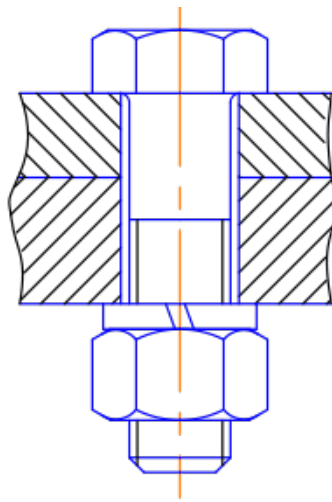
Corte de una placa unida por un tornillo con tuerca
